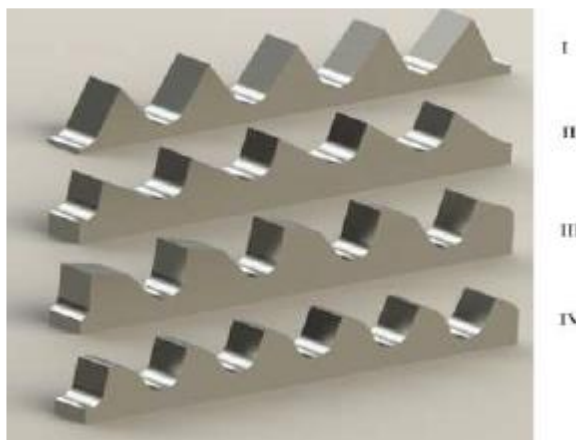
Типорозміри зубів пилок для різання гарячого
